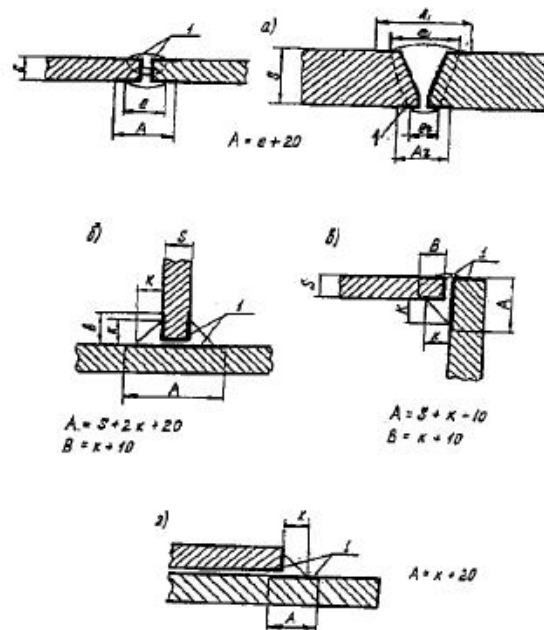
Зачистка кромок и поверхности металла перед сваркой соединений . а – стыковых , б – тавровых , в – угловых , г – нахлесточных , 1 – зоны зачистки .
